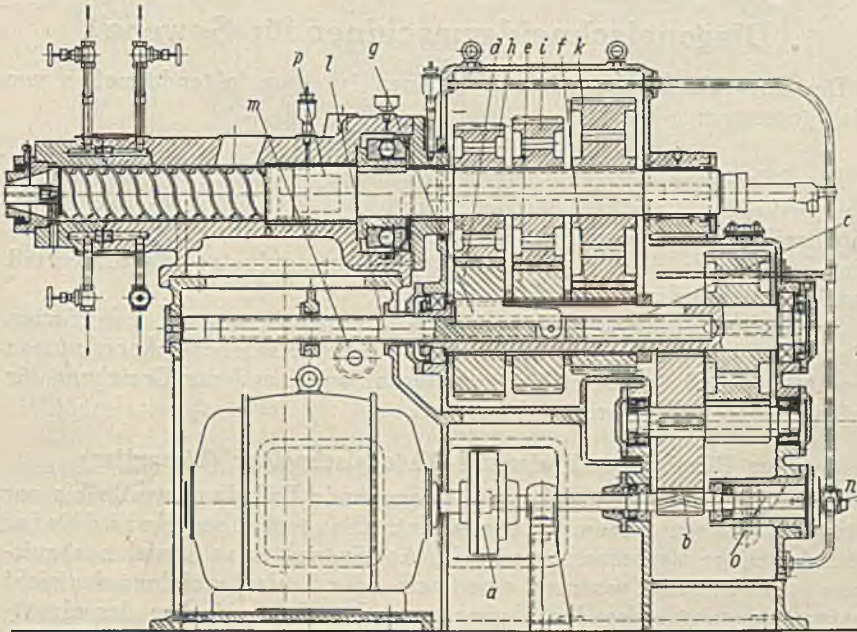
Schlauchmaschine, 150-mm-Schnecken mit Schaltgetriebe
